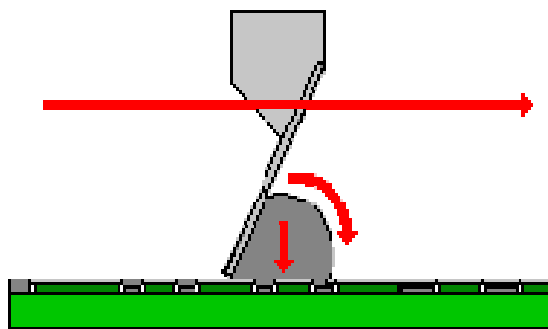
Modelo de la impresión de pasta de soldadura usando espátula.
